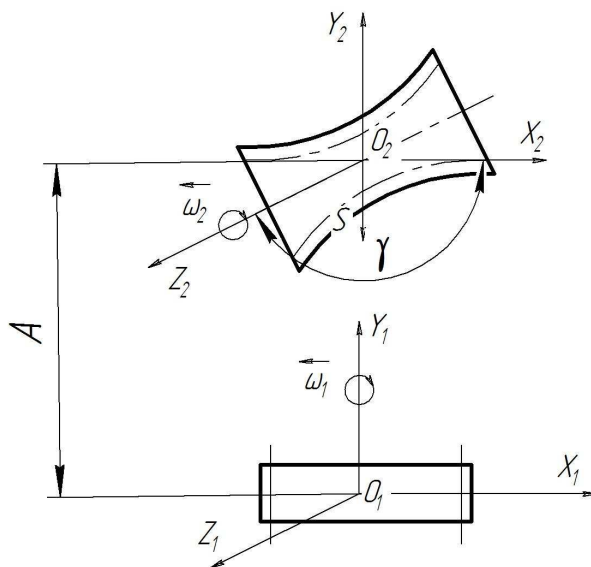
Схема притирки зубьев цилиндрического зубчатого колеса винтовым гиперболоидным притиром
